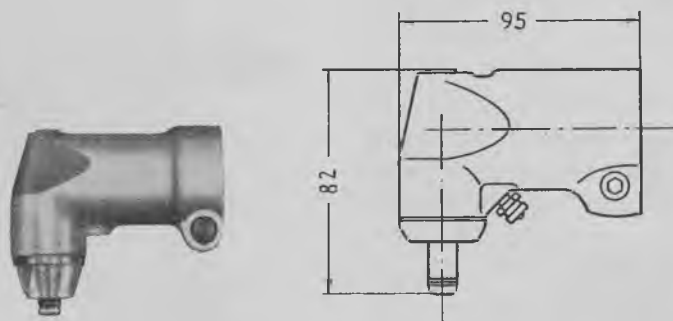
Skruerhoved til el-skruetrækker (til vinkelskrining). »Bosch«.
